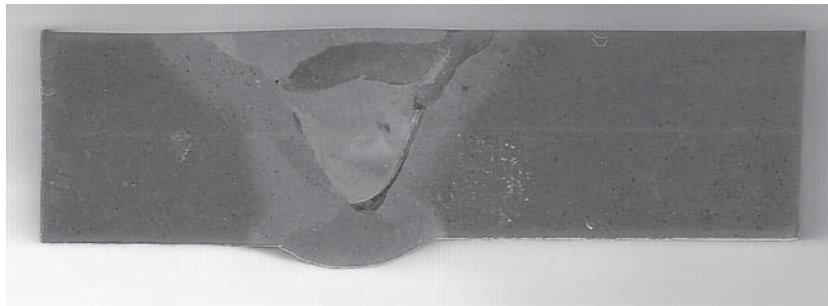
Soldadura de acero al carbón con falta de fusión lateral.
